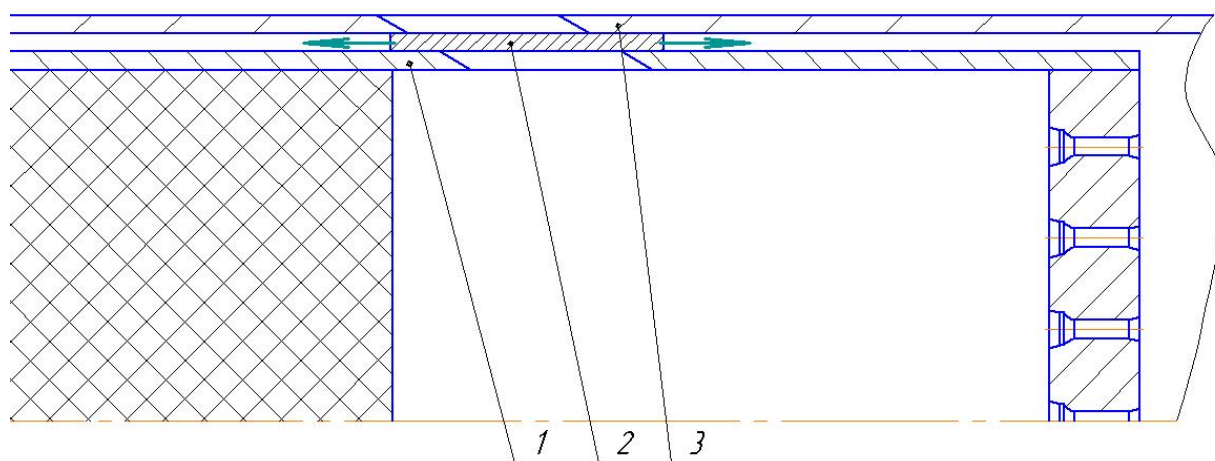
Схема выброса газов из газогенератора с помощью крышки на корпусе
